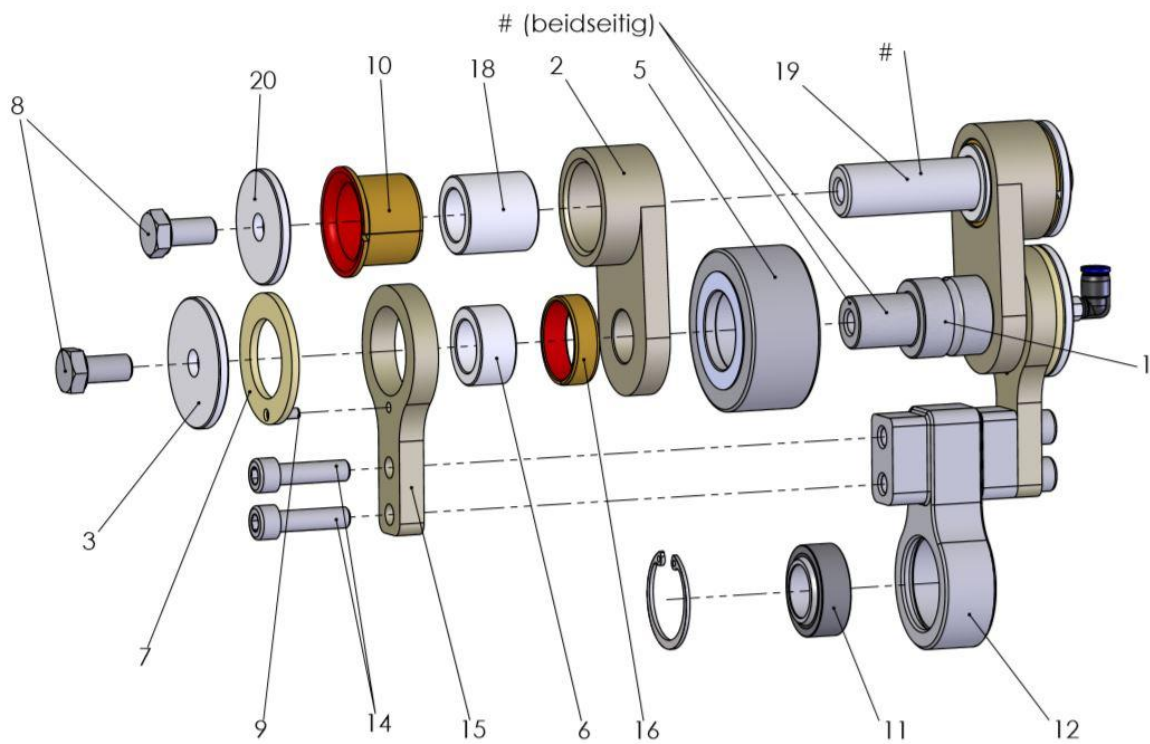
1: Explosionszeichnung Zweigelenkschwinge
